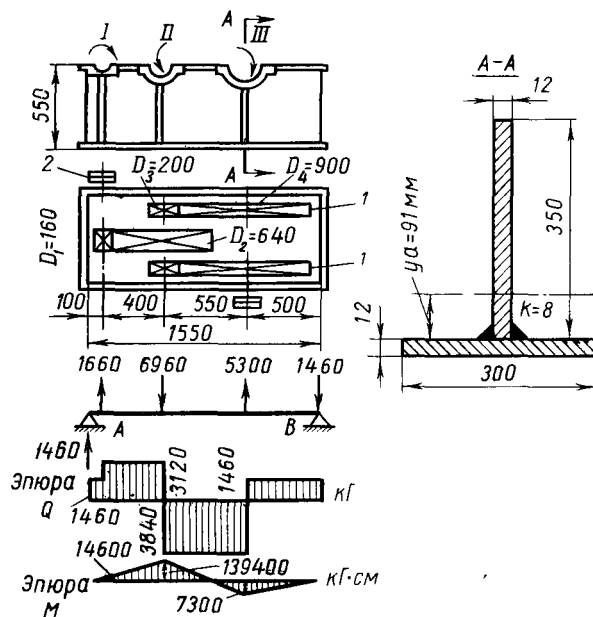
К примеру расчета рамы корпуса двухступенчатого редуктора
